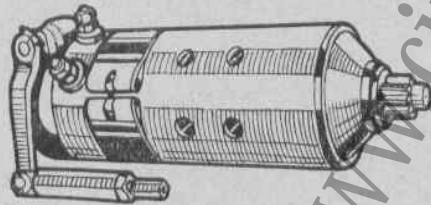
DÉMARREUR À PÉDALE, VUE EXTÉRIEURE.
